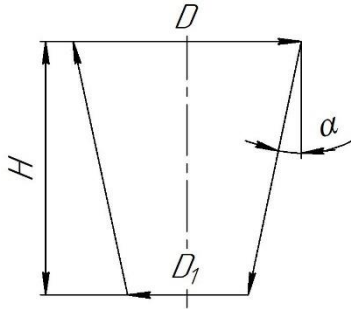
Детальний розмірний ланцюг пробки
